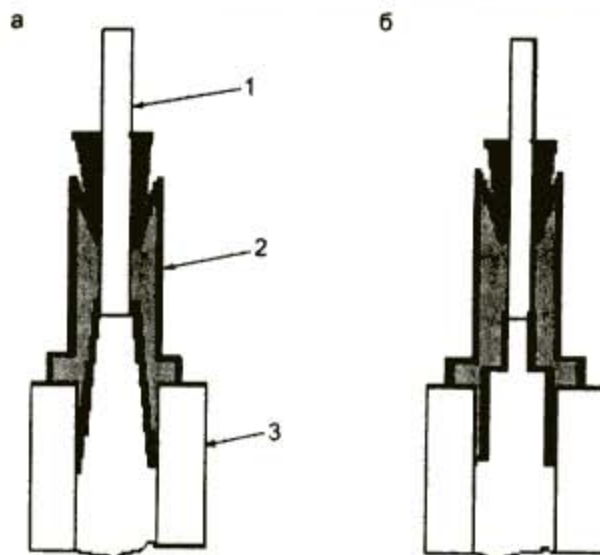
1 - трубка колонки; 2 - выходной штуцер пакера; 3 - корпус пакера.
